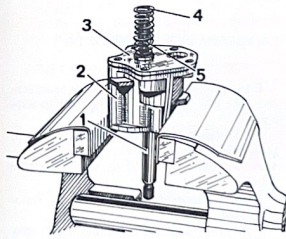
Conjunto del cuerpo de bomba de aceite con la válvula reguladora de presión.
